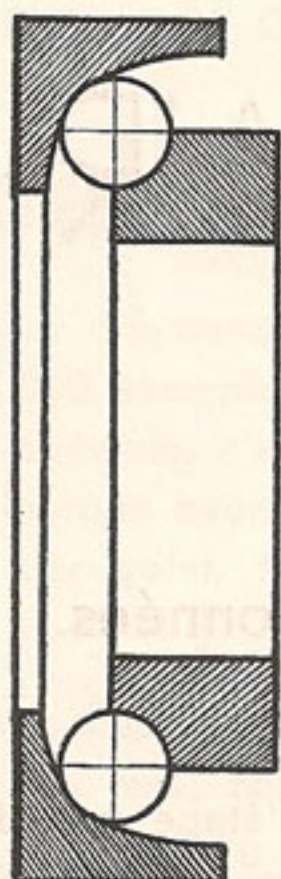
LE ROULEMENT A CONE ET CUVETTE.
